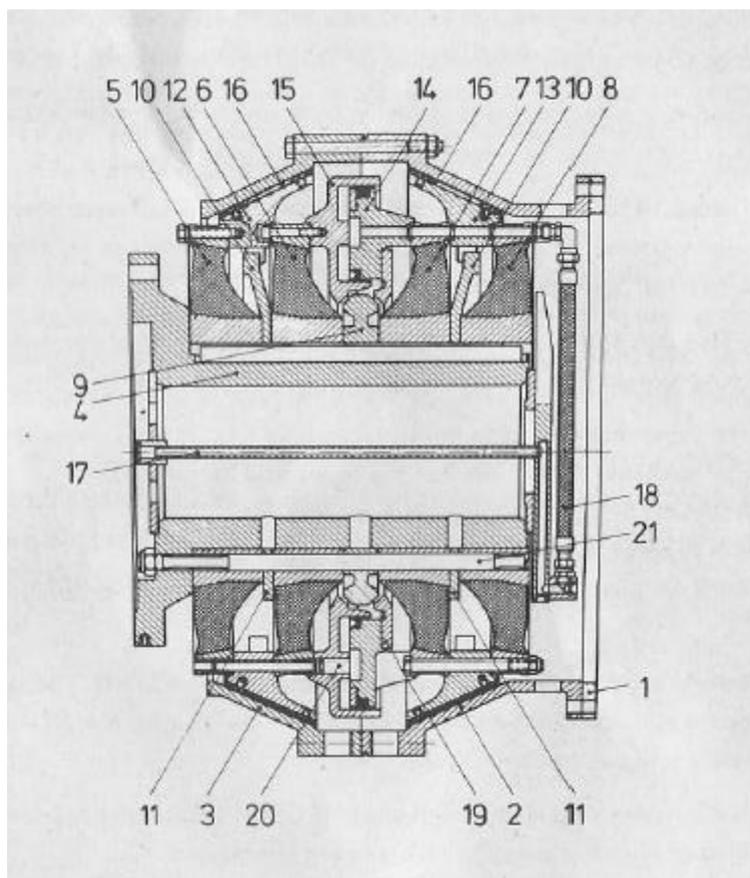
Plano embrague Lothman. Fuente: [13]
